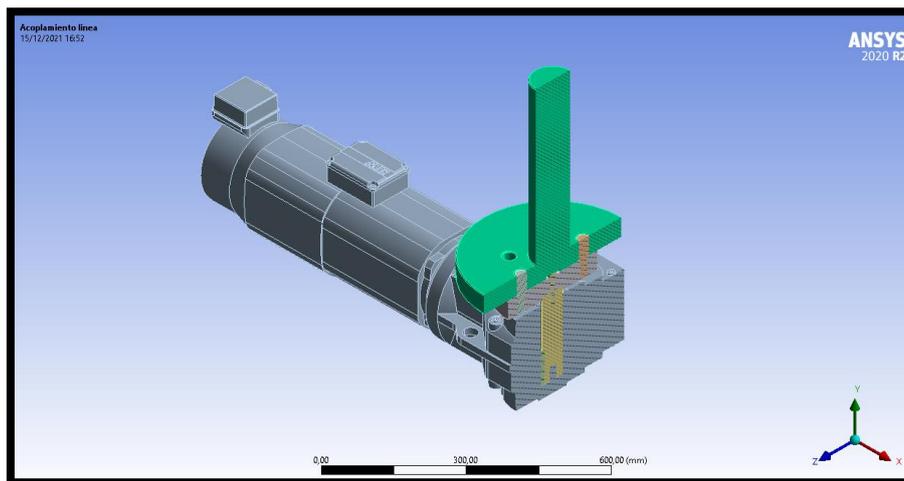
Corte por sección de vista isométrica del conjunto en Ansys.
